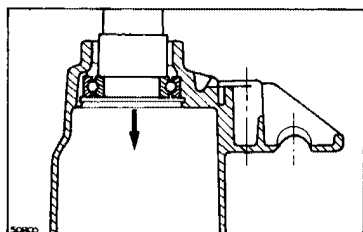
Выпрессовка подшипника центральной (полуосевой) шестерни дифференциала
